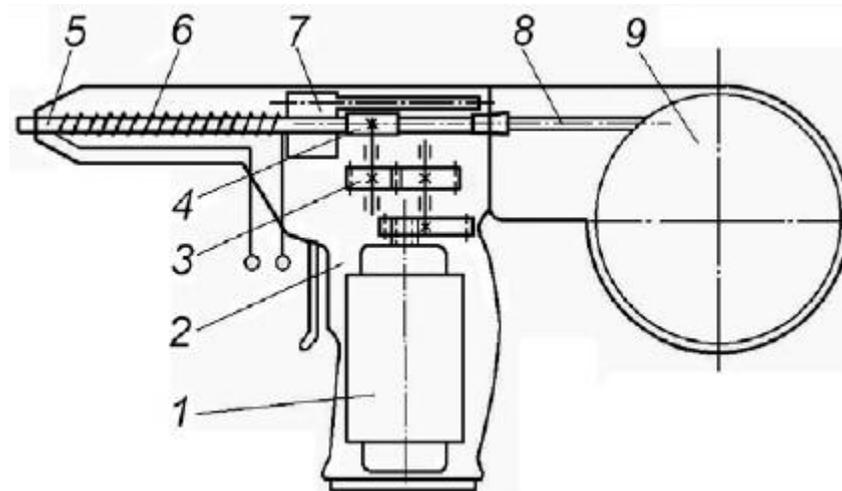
Схема пистолета-экструдера прямооточного типа: 1 – электродвигатель; 2 – рукоятка; 3 – редуктор; 4 – подающие ролики; 5 – цилиндр; 6 – электронагреватель; 7 – охладитель; 8 – присадочный пруток; 9 – кассета с присадочным материалом
